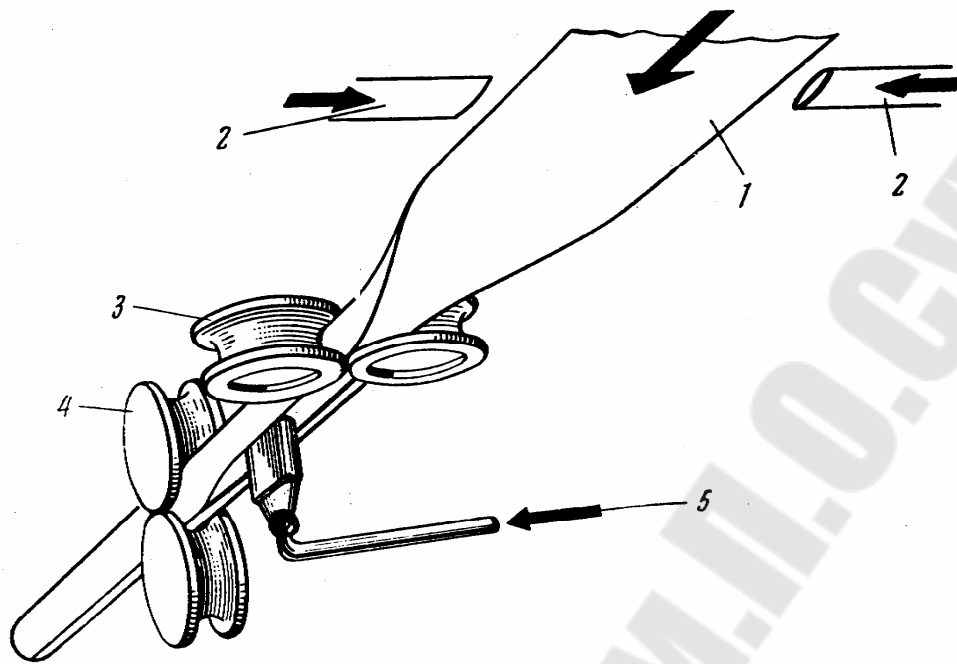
Схема формовки штрипса в трубу при непрерывной печной сварке: 1 – штрипс; 2 – первичная обдувка воздухом кромок; 3 – вертикальные формующие валки; 4 – горизонтальные сварочные валки; 5 – вторичная обдувка воздухом кромок
